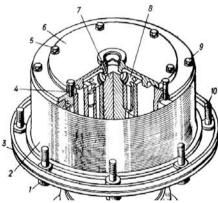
Снятие водила, полуосей: 1 — гайка; 2 — водило; 3, 4 — прокладка; 5, 10 — болт; 6 — крышка; 7 — полуось; 8 — колесо зубчатое; 9 — пробка
